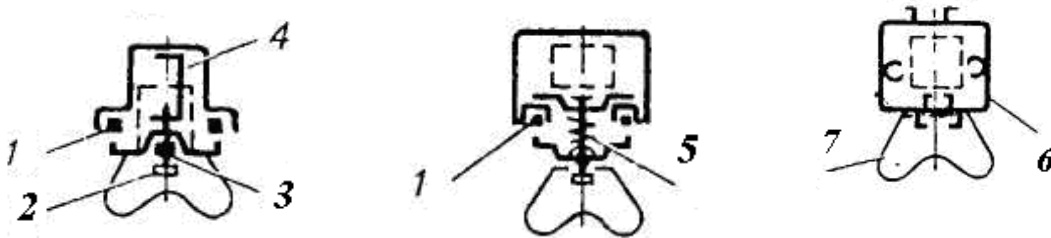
Ущільнені СП із ЛЛ: а) 1 – гумове ущільнення; 2 – кріпильний невинятковий болт; 3 – поворотна клямка; 4 – скоба кріплення розсівача; б) 1 – гумове ущільнення; 5 – пружина; в) цілісні конструкції корпусу: 6 – пресований корпус; 7 – патрон з ущільненням по колбі ЛЛ
